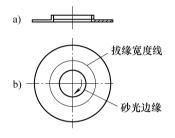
内拔缘零件、毛料 a) 零件 b) 毛料
